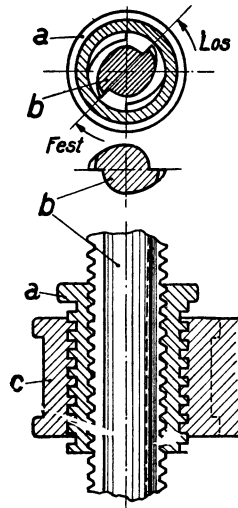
Bügelschraubzwinde, Schnitte.
